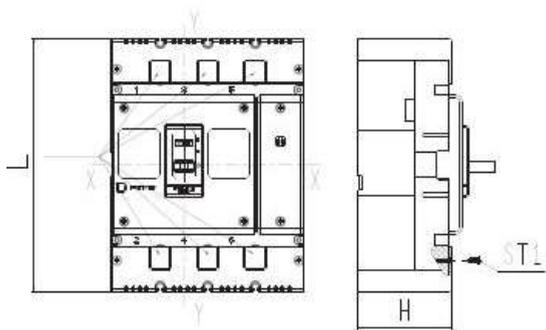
Габаритные размеры крышек клеммника коротких KK-300Rc
